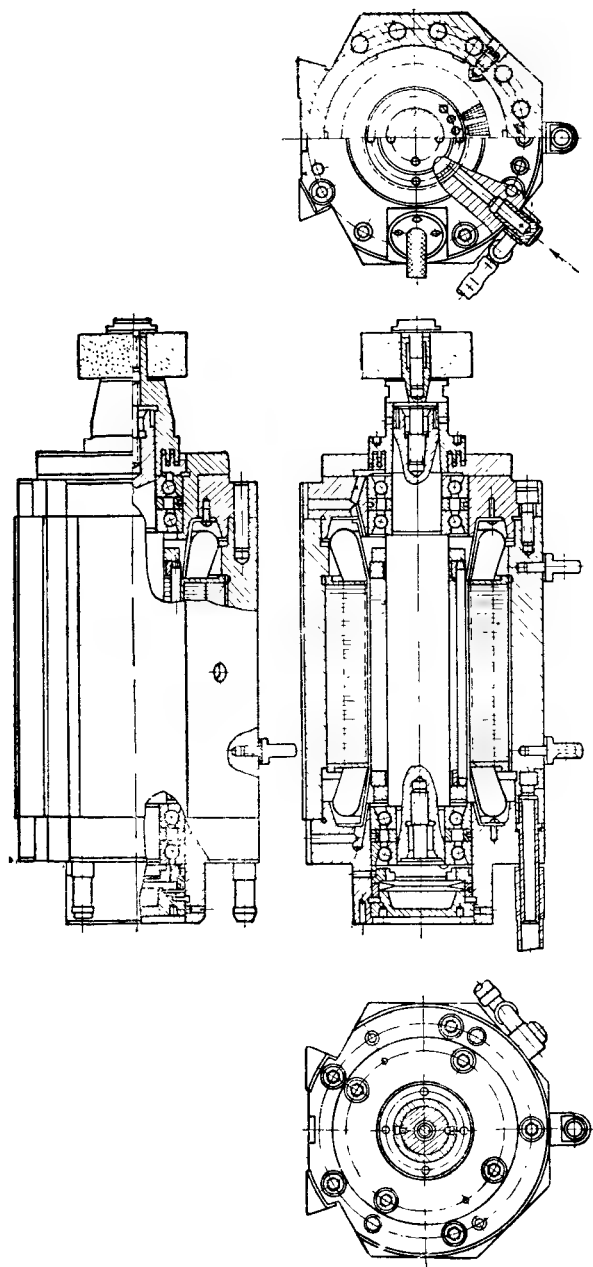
Вид в разрезе электрошпинделя ЭШ-12/5,0 новой конструкции с водяным охлаждением в корпусе.
